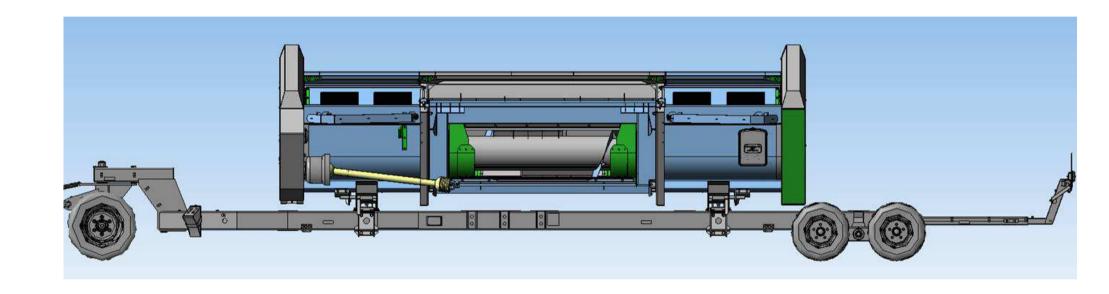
Приспособление для перемещения адаптеров ППА-4000 "Uni Cart 4000" с установленной жаткой RSM SS-490 (с комплектом для транспортировки SS-490.13.00.000A).
